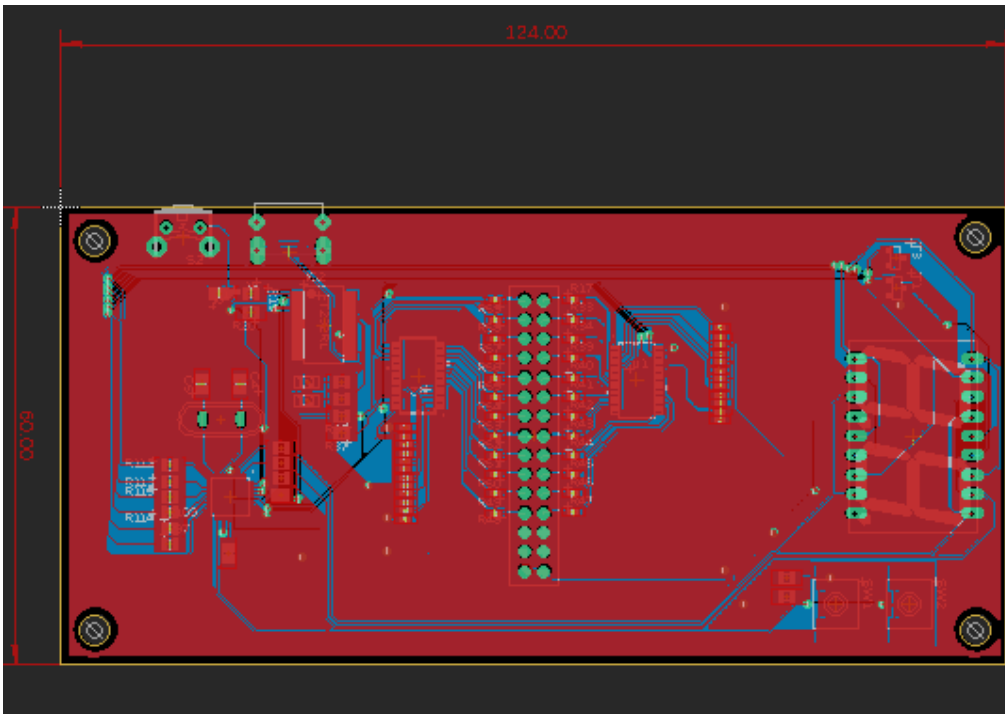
Diseño tarjeta PCB de control vista desde el comando Ratsnests. Tobón. (2019)
